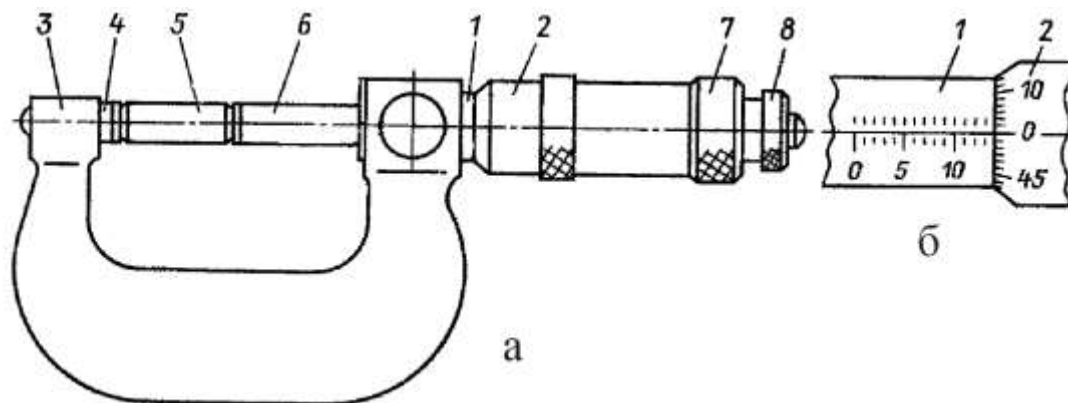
Мікрометр (а) і його шкала (б): 1 – стебло; 2 – барабан; 3 – скоба; 4 – п'ята; 5 – установлювальна міра; 6 – мікрогвинт; 7 – установочний ковпачок; 8 – тріскачка
